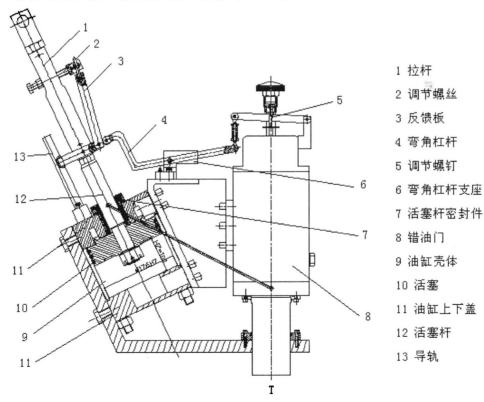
油动机总成机构 Fig. 3.5 Oil motor assembly mechanism
